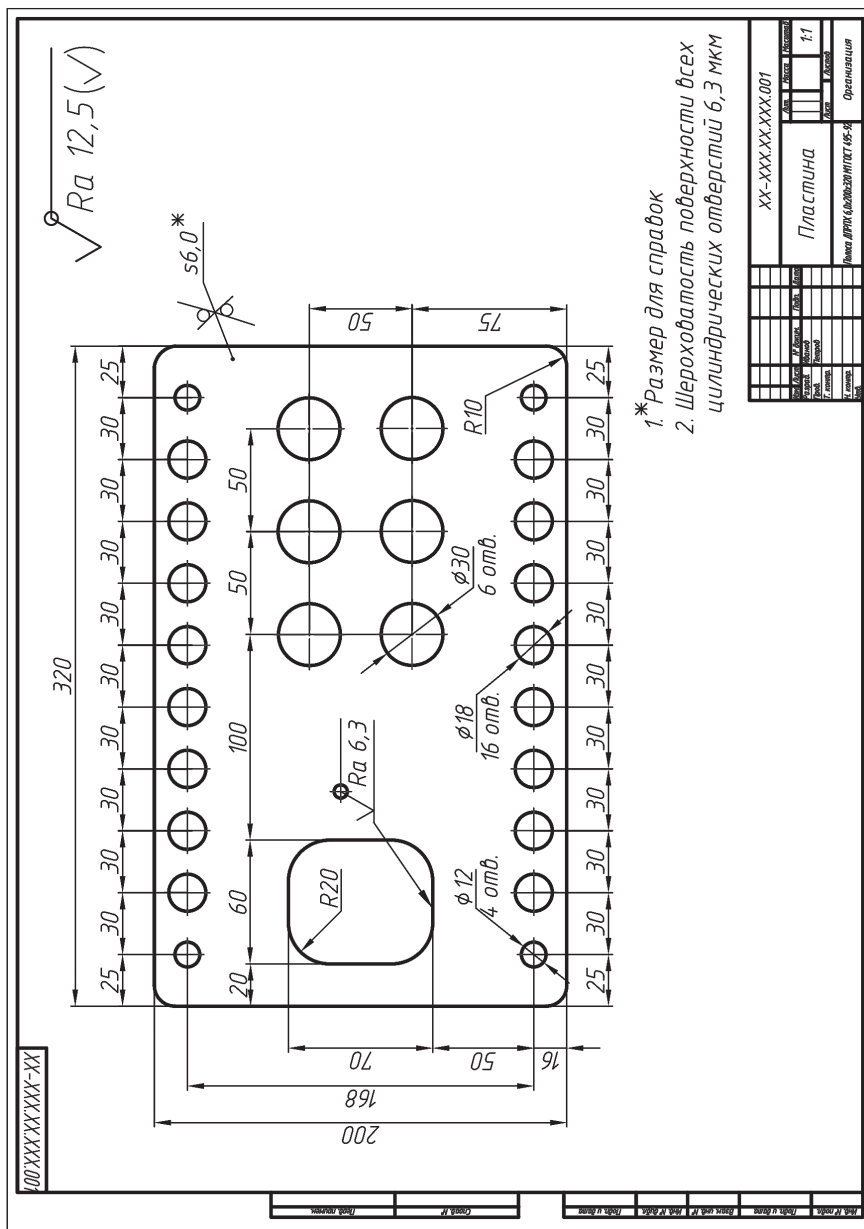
Чертеж детали «Пластина» перед заливкой отверстий
